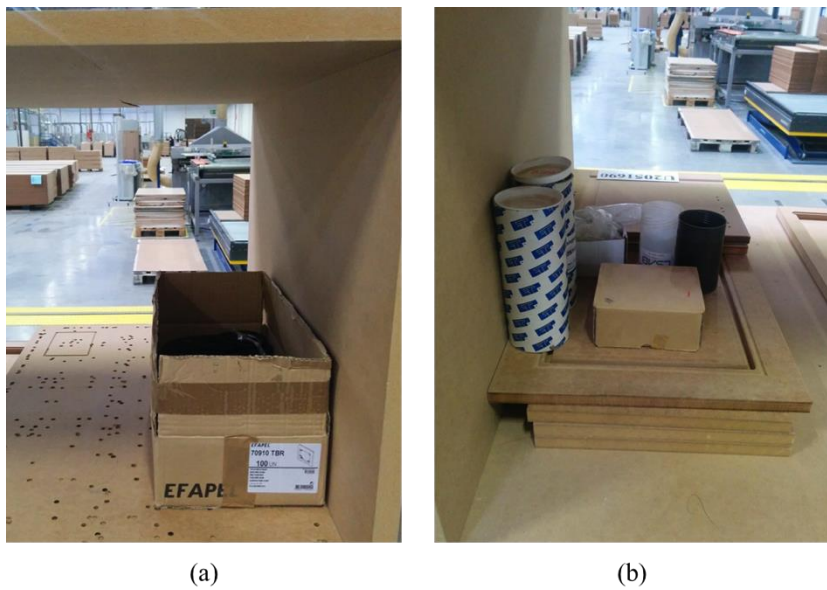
a) Borrachas de diferentes dimensões. b) Vedação do molde
